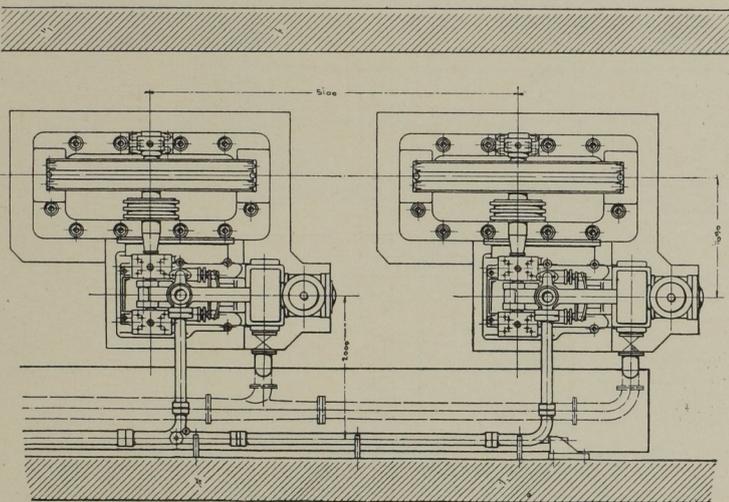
Grundriss der Pumpen und Motoren. Masst. 1:100.
